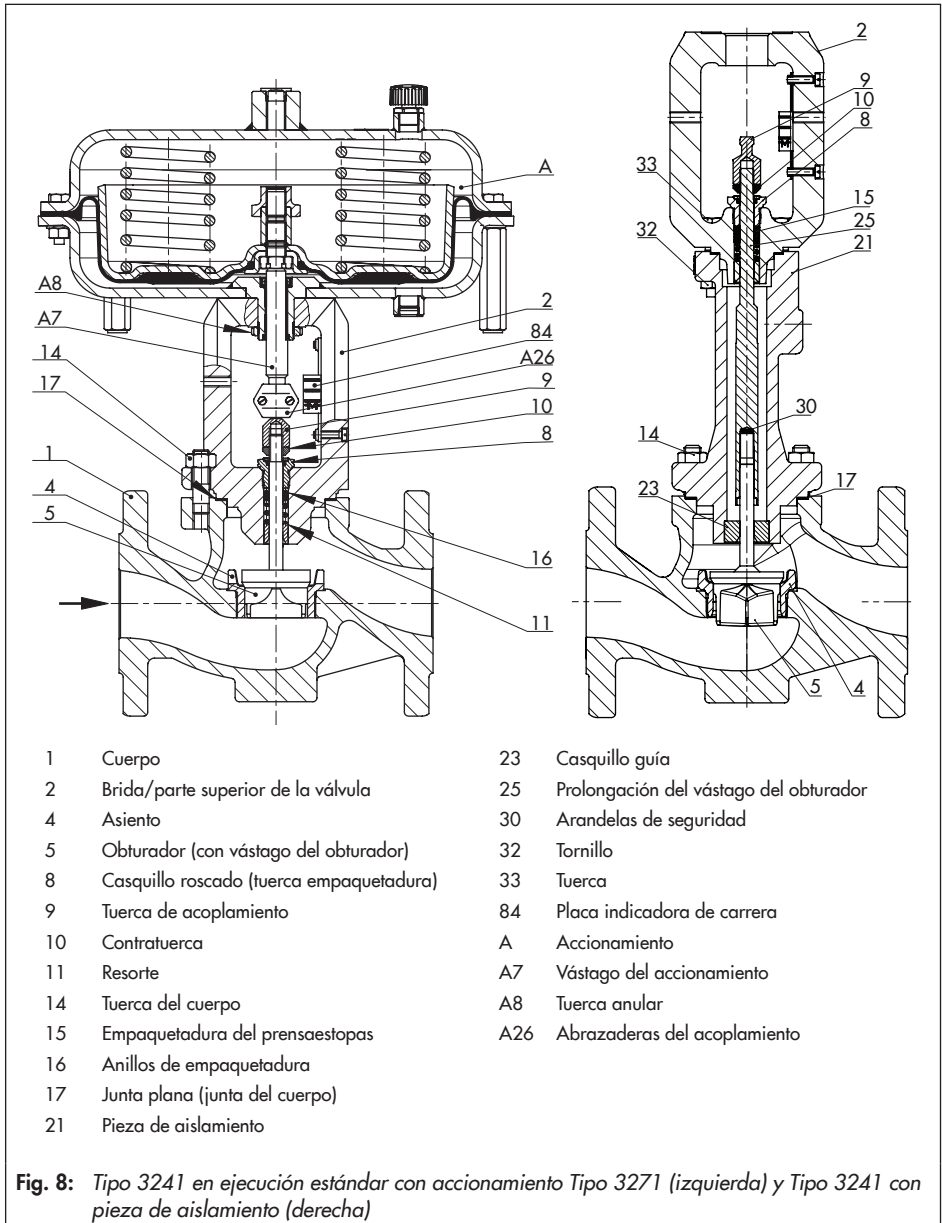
Tipo 3241 en ejecución estándar con accionamiento Tipo 3271 (izquierda) y Tipo 3241 con pieza de aislamiento (derecha)
